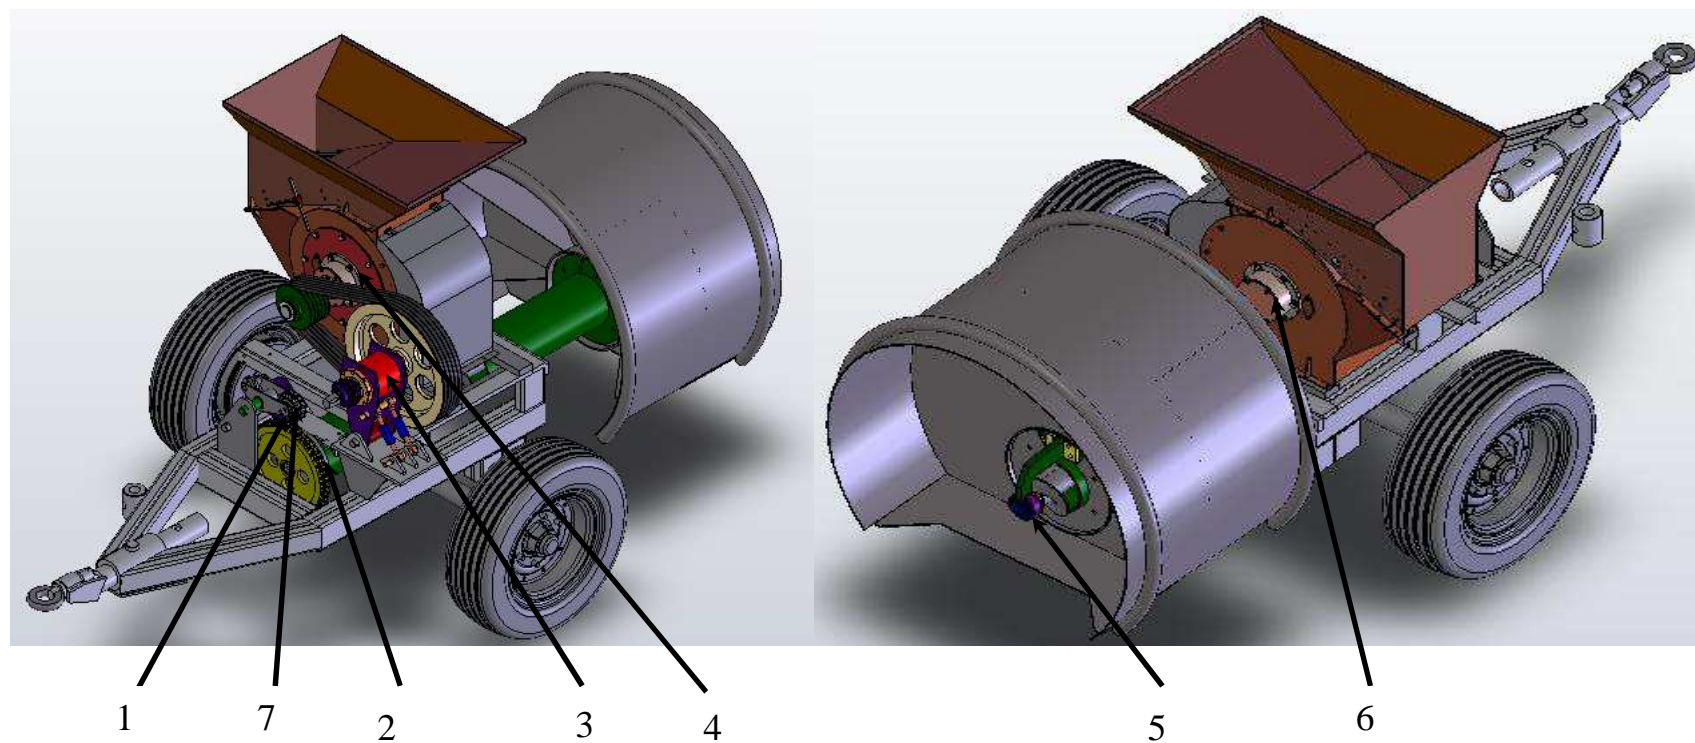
Схема смазки и схема размещения подшипников
